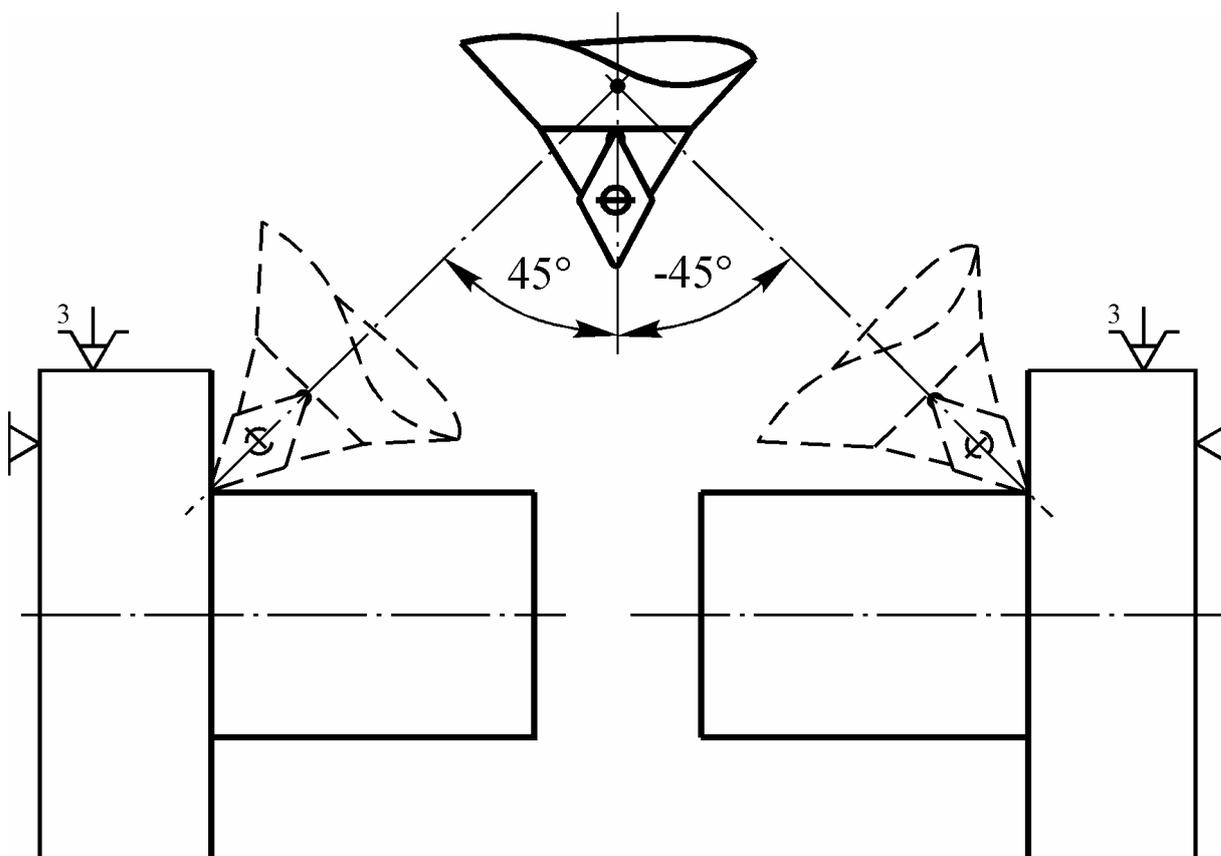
Схема последовательной обработки детали в главном и контршпинделях резцовой головкой
